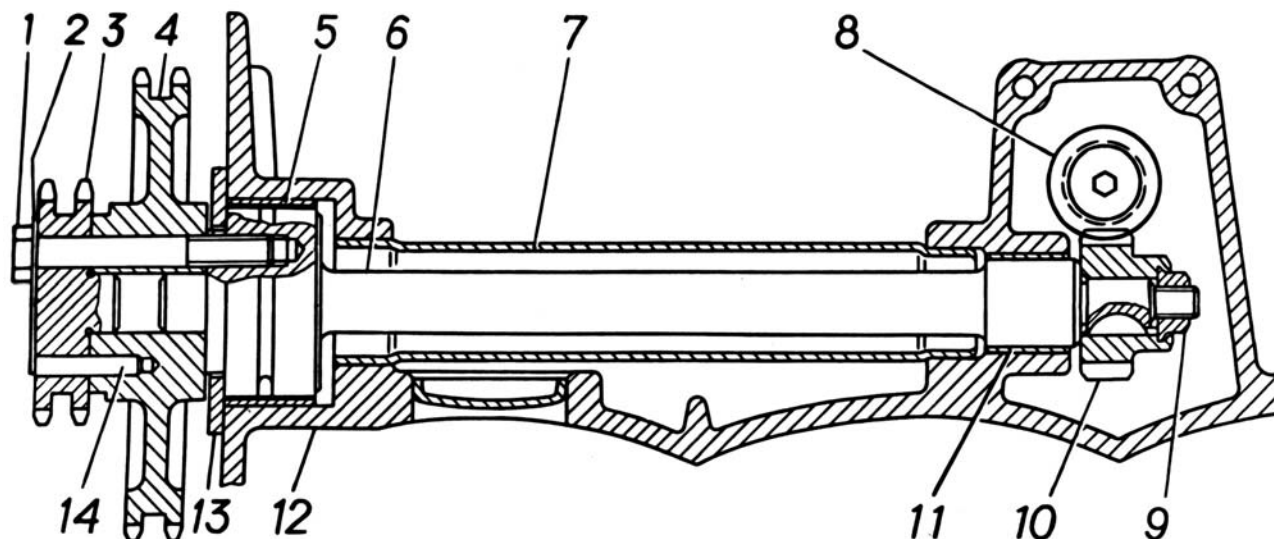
Промежуточный вал: 1 - болт; 2 - стопорная пластина; 3 - ведущая звездочка; 4 - ведомая звездочка; 5 - передняя втулка вала; 6 - промежуточный вал; 7 - труба промежуточного вала; 8 - шестерня ведомая привода масляного насоса; 9 - гайка; 10 - шестерня ведущая привода масляного насоса; 11 - задняя втулка вала; 12 - блок цилиндров; 13 - фланец промежуточного вала; 14 - штифт
